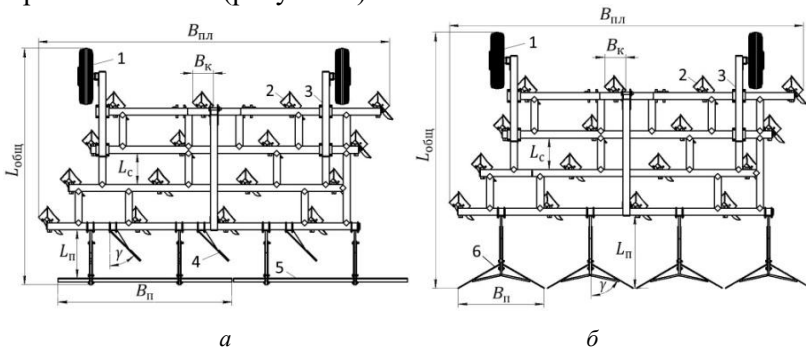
Конструктивно-технологическая схема навесного секционного плуга с приспособлениями: *a* - № 1; *б* - № 2; L_c – длина секции; $L_{пл}$, $B_{пл}$ – длина и ширина приспособлений; $L_{общ}$ – общая длина плуга; 1 – колесный узел; 2 – корпус плуга; 3 – рама плуга; 4, 6 – стalkerватели; 5 – выравниватель пашни
